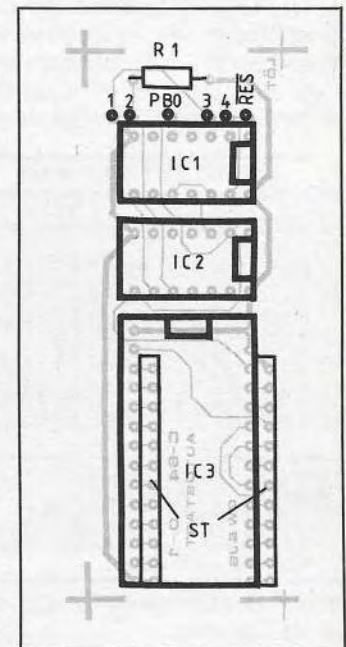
Der Bestückungsplan zum Layout aus Bild 10
